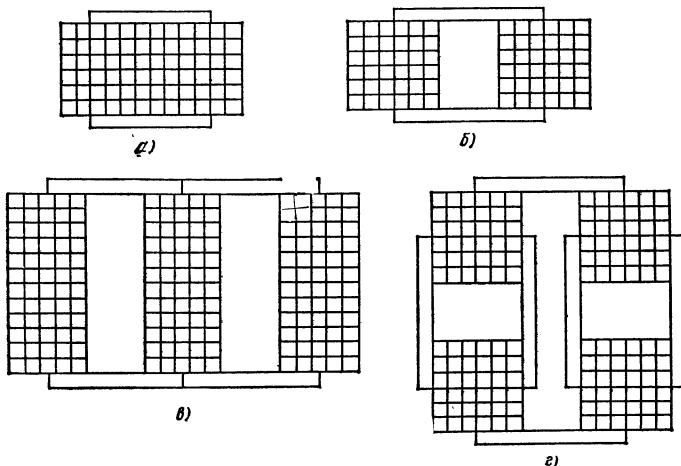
Каркасные конструкции сборных оснований приспособлений:
